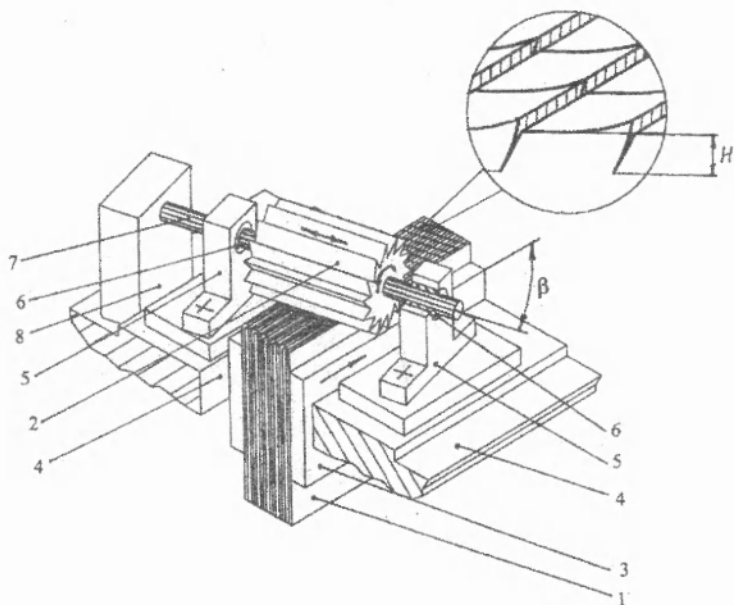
Схема пристрою утворення рельєфу на корінці книжкового блока для клейового скріплення друкованої продукції: 1 – книжковий блок; 2 – циліндрична фреза; 3 – транспортуючий пристрій; 4 – станина; 5 – кронштейни; 6 – підшипникові вузли; 7 – вісь; 8 – електромагніт
